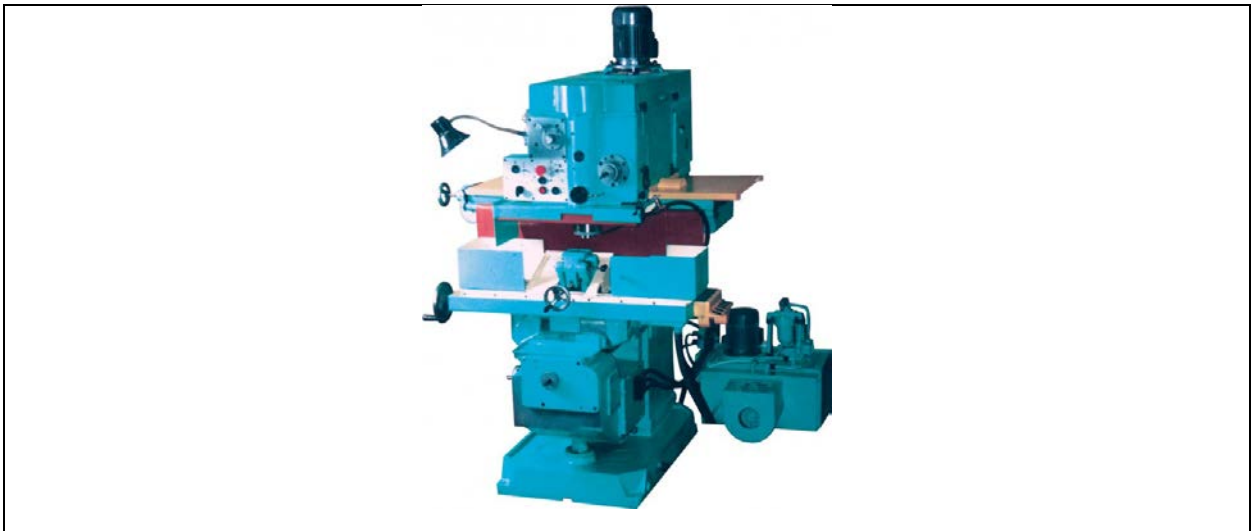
Шпонково-фрезерний верстат моделі 692Д
